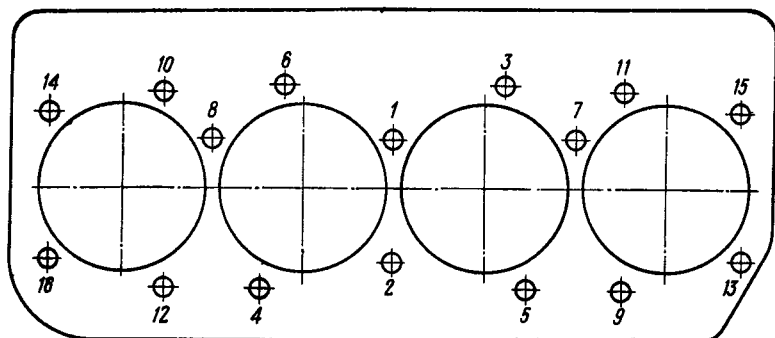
Схема последовательности затяжки гаек шпилек крепления головки цилиндров.
